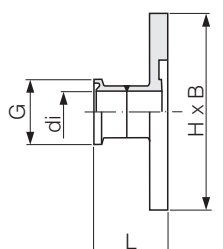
Vista frontal con dimensiones del sensor DN 4...15
